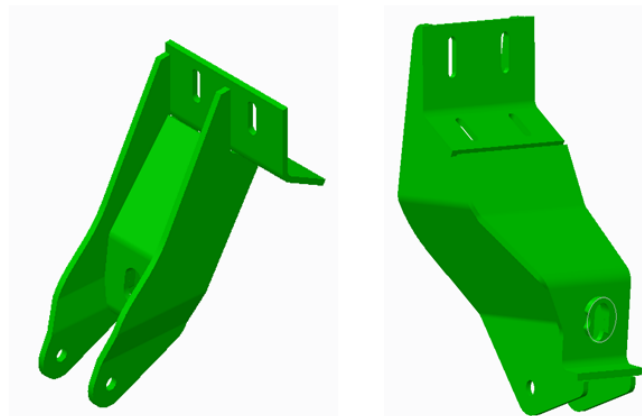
Conjuntos soldados dos suportes do sistema de corte de palha
